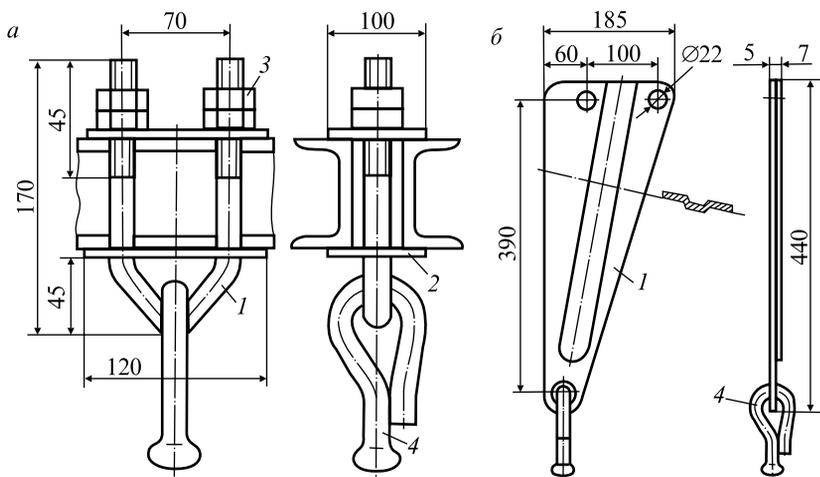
Бугель: *a* — из прутка  $d = 16$  мм; *б* — пластинчатый; 1 — бугель; 2 — планка; 3 — гайка; 4 — серьга сварная
